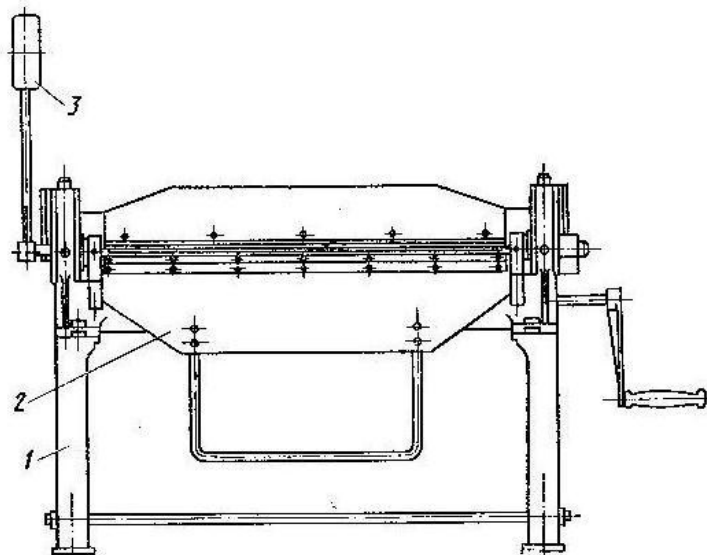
Кромкогибочный станок КГС-1, 5×1000:
